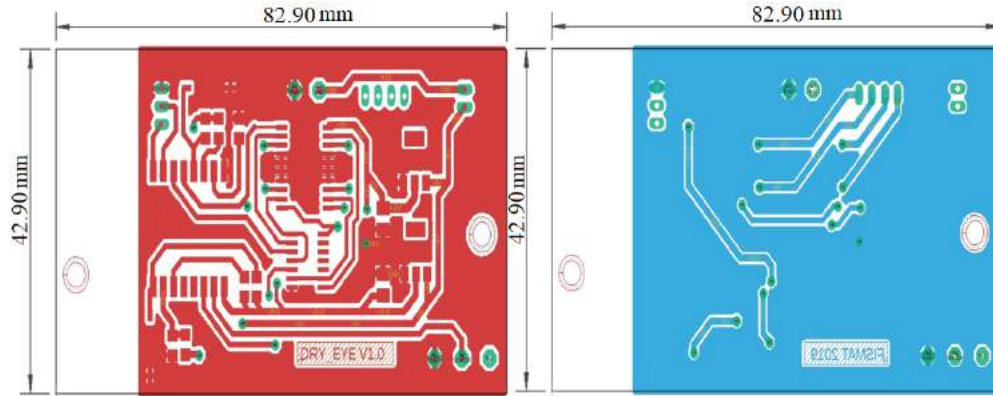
Diseño de la placa PCB del dispositivo de microinyección. A la izquierda pistas de arriba y a la derecha pistas de abajo.
